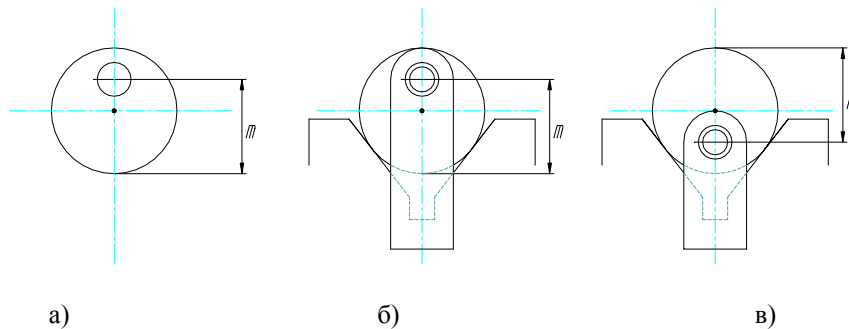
Варианты конструкции сверлильного приспособления - кондуктора.
